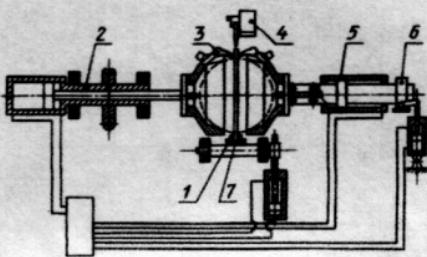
Схема станка - автоматика для сборки и сварки пустотелых шаров из двух полусфер
